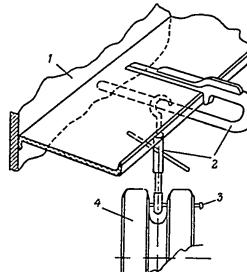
Приспособление для снятия опорного катка: 1 — борт танка; 2 — приспособление; 3 — палец трака; 4 — каток
